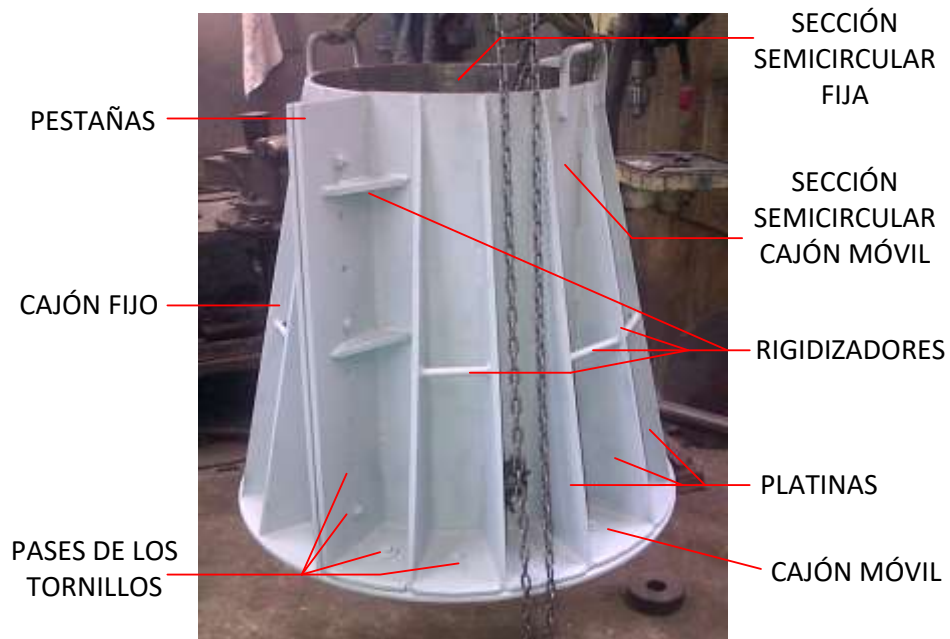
Caja metálica ensamblada. Fuente: Propia.
